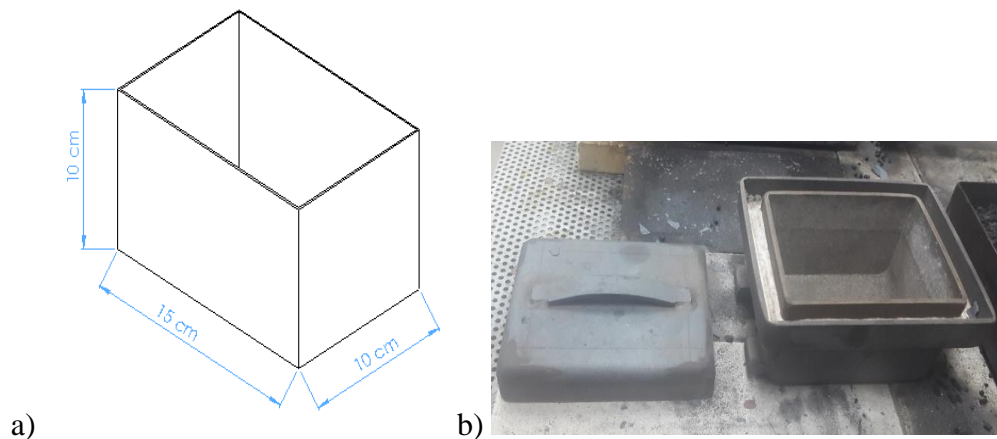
Caja de hierro fundida a) Dimensiones, b) Forma física
